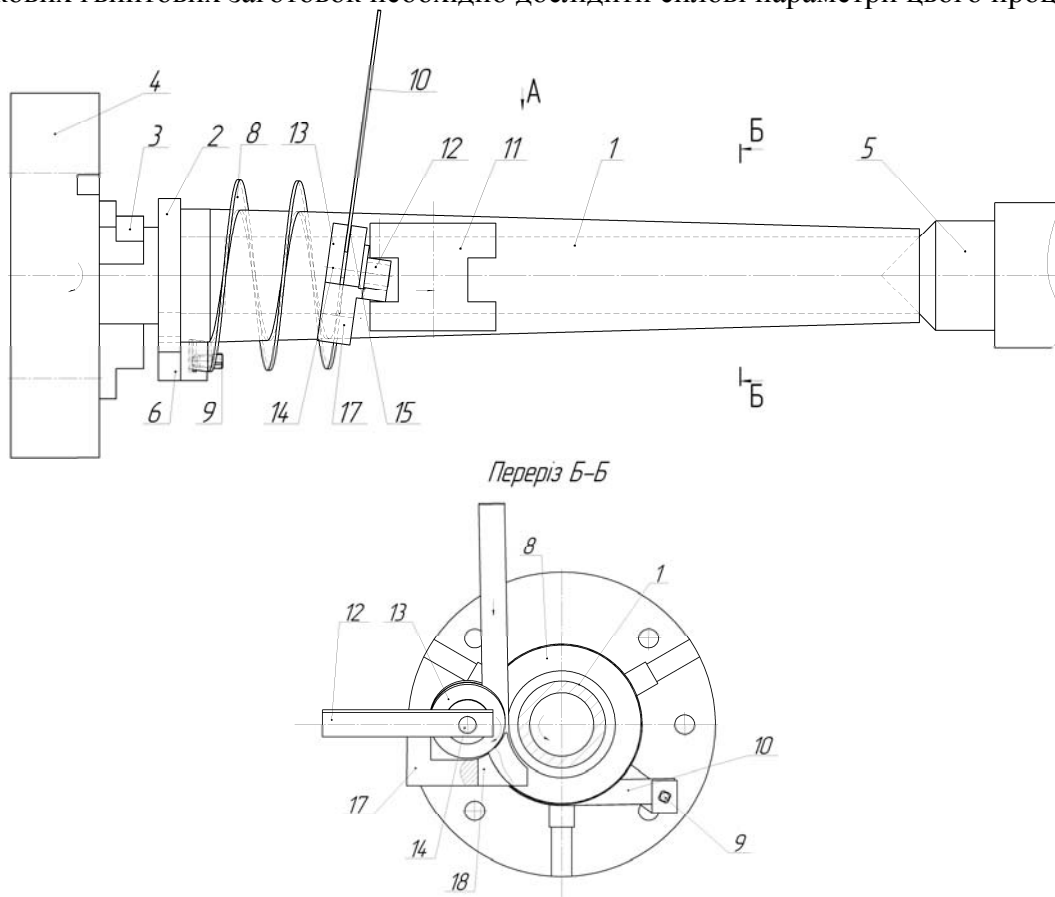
Пристрій для навивання стрічкових гвинтових заготовок: 1 – оправа; 2 – оправа; 3 – кулачок; 4 – патрон; 5 – центр; 6 – державка; 8 - стрічкова гвинтова заготовка; 9 – механізм затиску; 10 – стрічка; 11 – різцетримач; 12 – державка; 13 – формувальний ролик; 14 – вісь; 15 - паз формувального ролика; 17 – державка; 18 - паз державки
